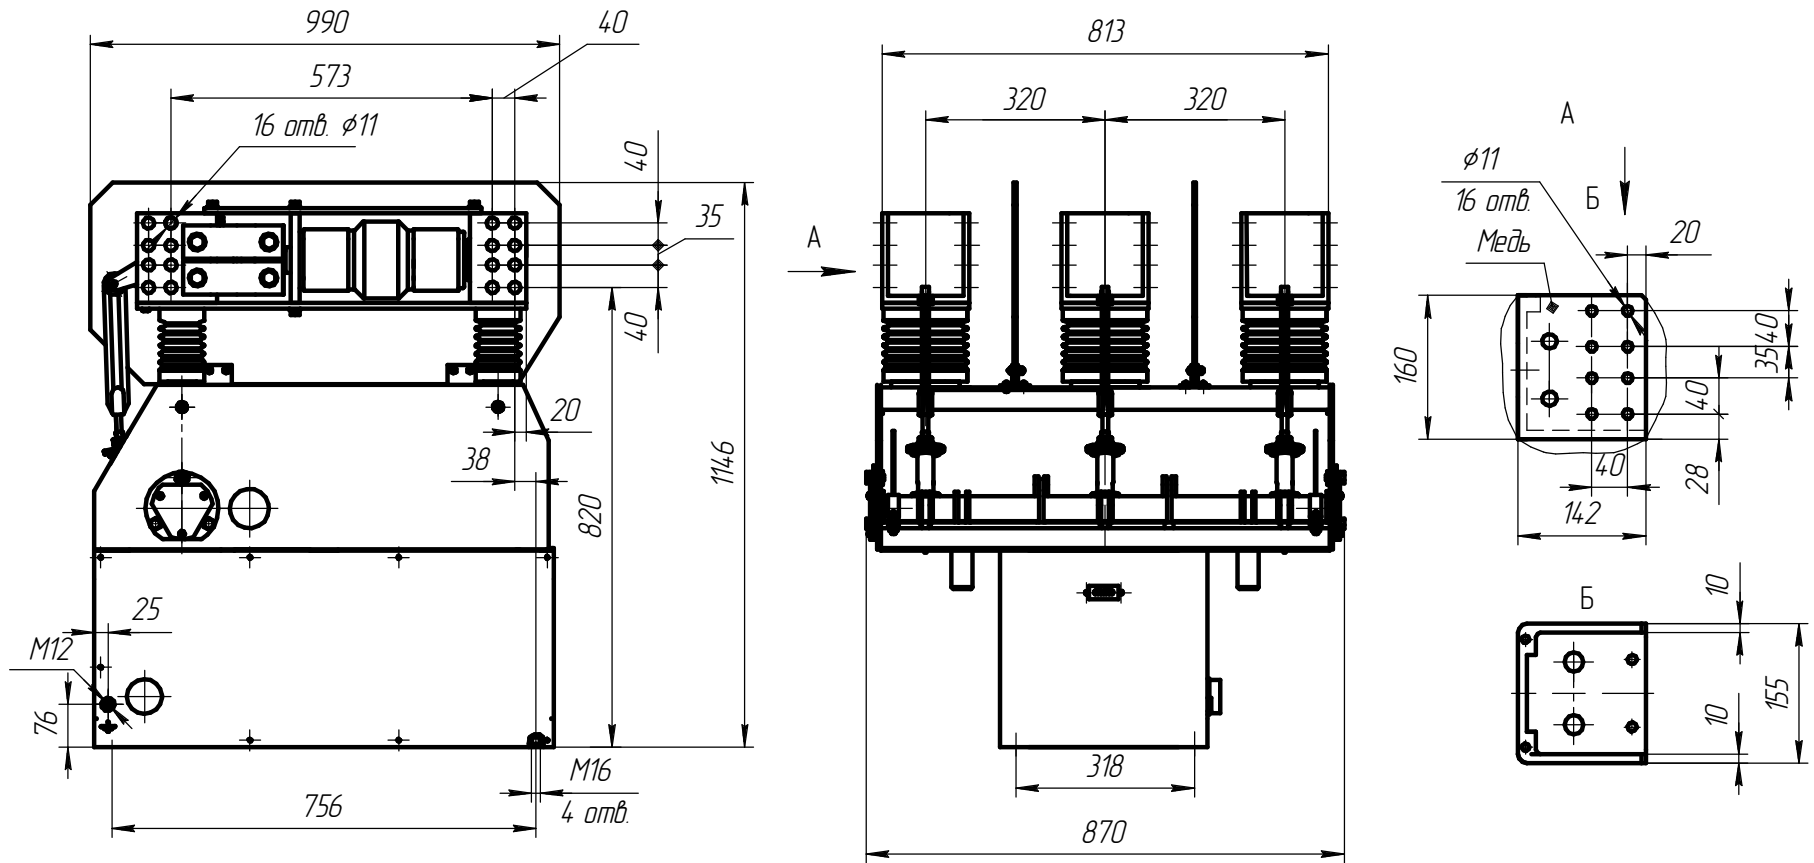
Габаритные, присоединительные и установочные размеры выключателя ВГГ-10 для проектирования новых типов распределительных устройств.
